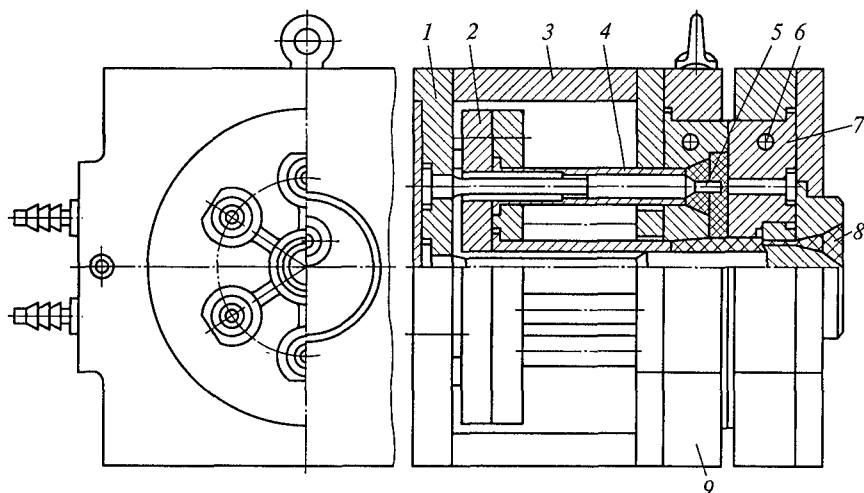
Пресс-форма для изготовления моделей в массовом производстве:
